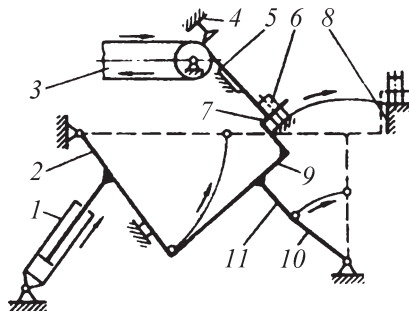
Манипулятор для подачи заготовок от индуктора на первую позицию штампа
